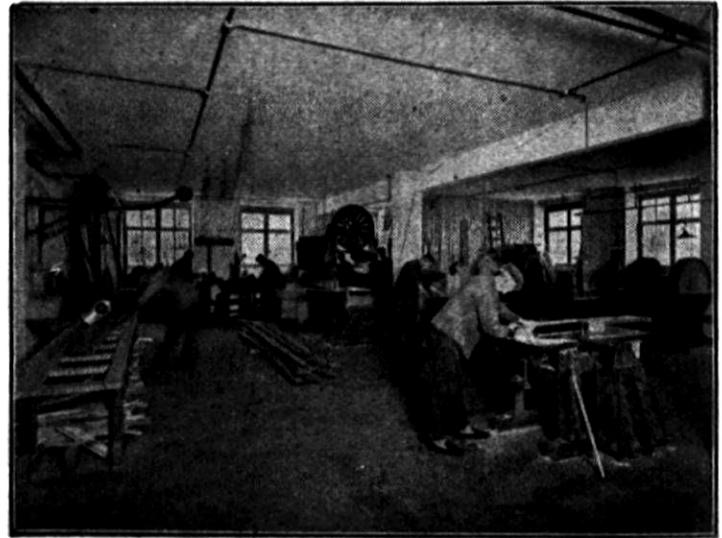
Teilansicht: Maschinensaal für Holzbearbeitung.
